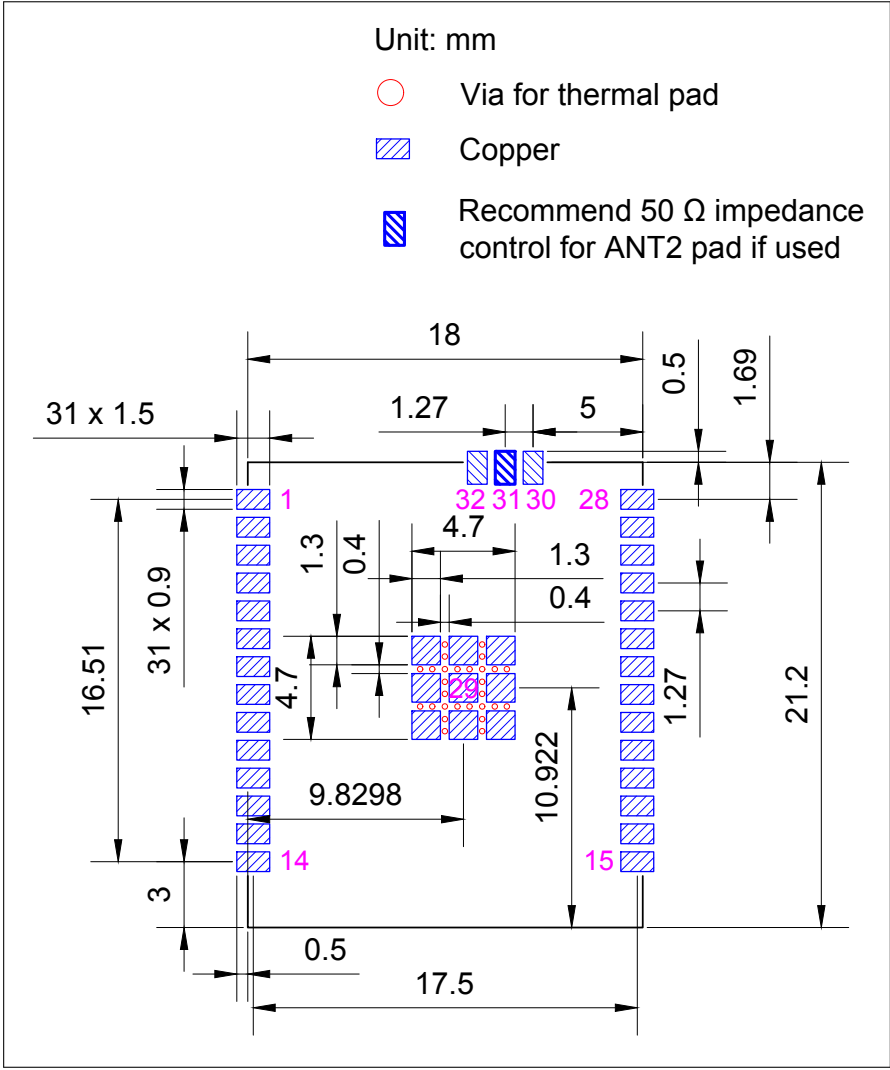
ESP32-C5-WROOM-1U 推荐 PCB 封装图形
